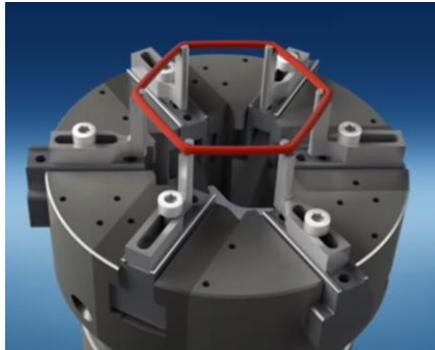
Sistema de colocación de juntas. Fuente:web
